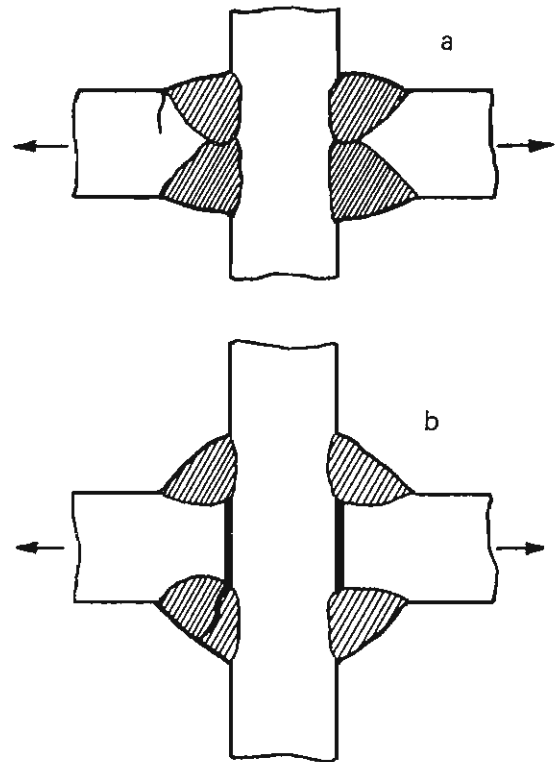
Fissuration par fatigue d'une soudure en croix à âme interrompue.
